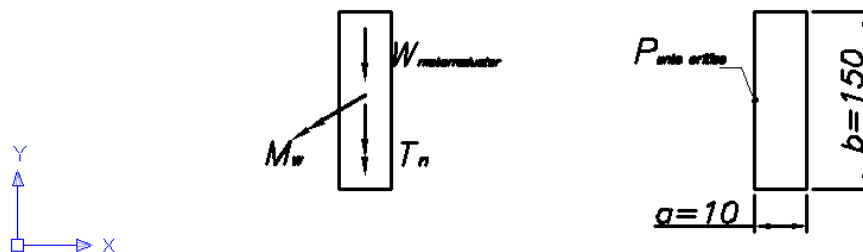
Izquierda: estado de cargas en la sección transversal de la plancha. Derecha: punto crítico y cotas de la plancha.
